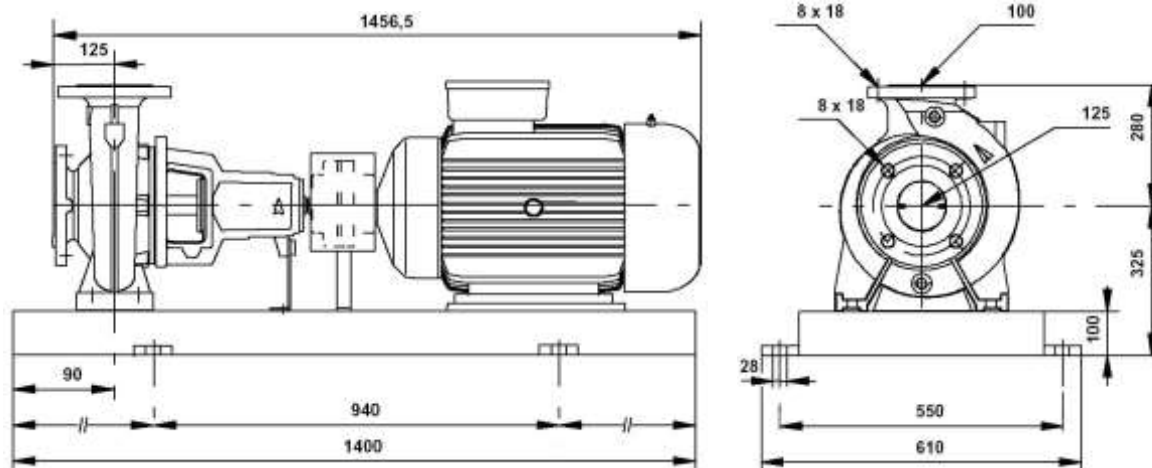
Насос с двигателем с установочными и габаритными размерами
